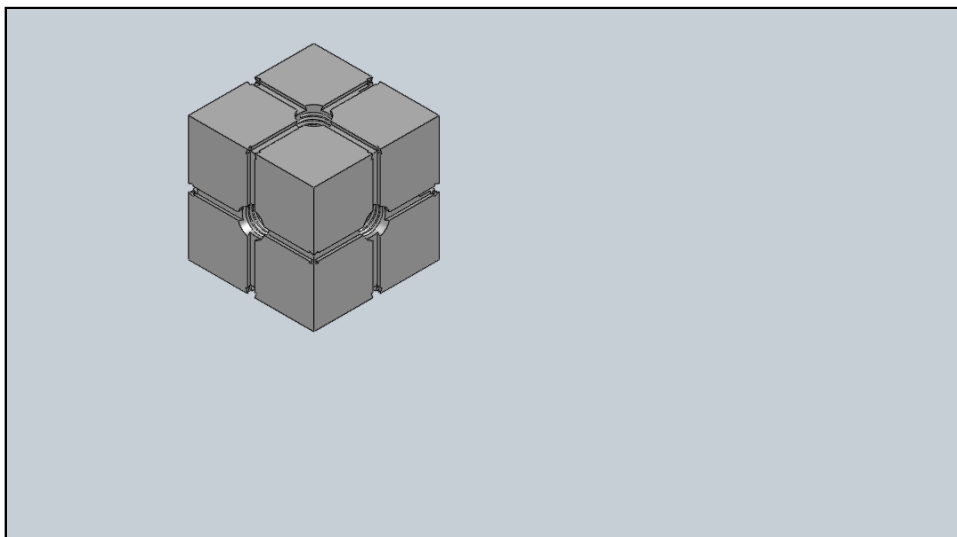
Montagem do conector e fixação ao elemento de ligação entre conectores.
